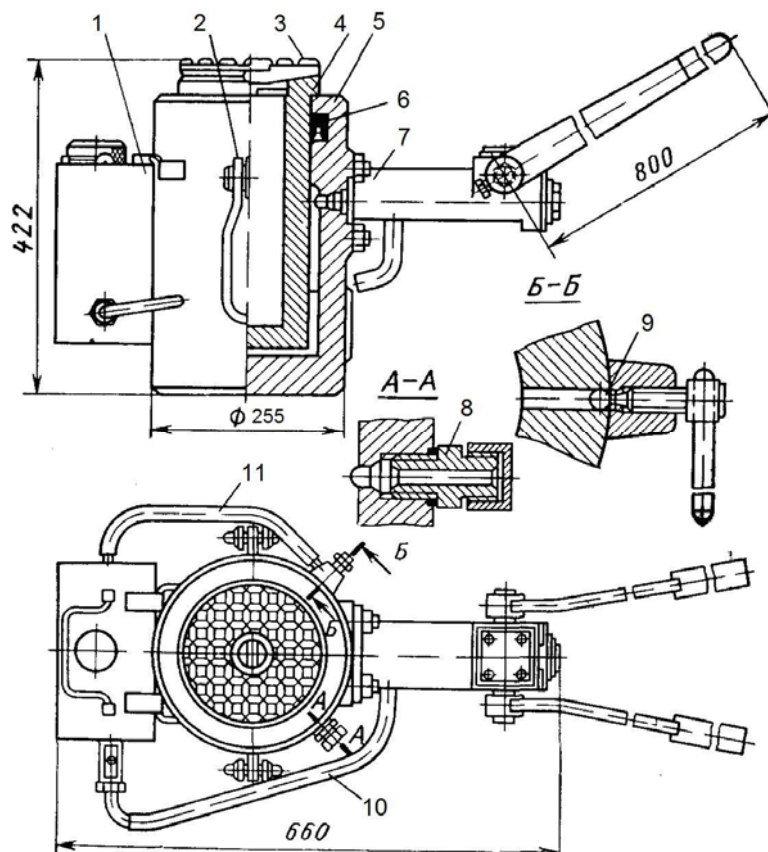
Гидравлический домкрат грузоподъемностью 100 т: 1 – бачок; 2 – ручка; 3 – пята; 4 – поршень; 5 – цилиндр; 6 – манжета; 7 – насос; 8 – штуцер манометра; 9 – шариковый клапан; 10 и 11 – трубопроводы
